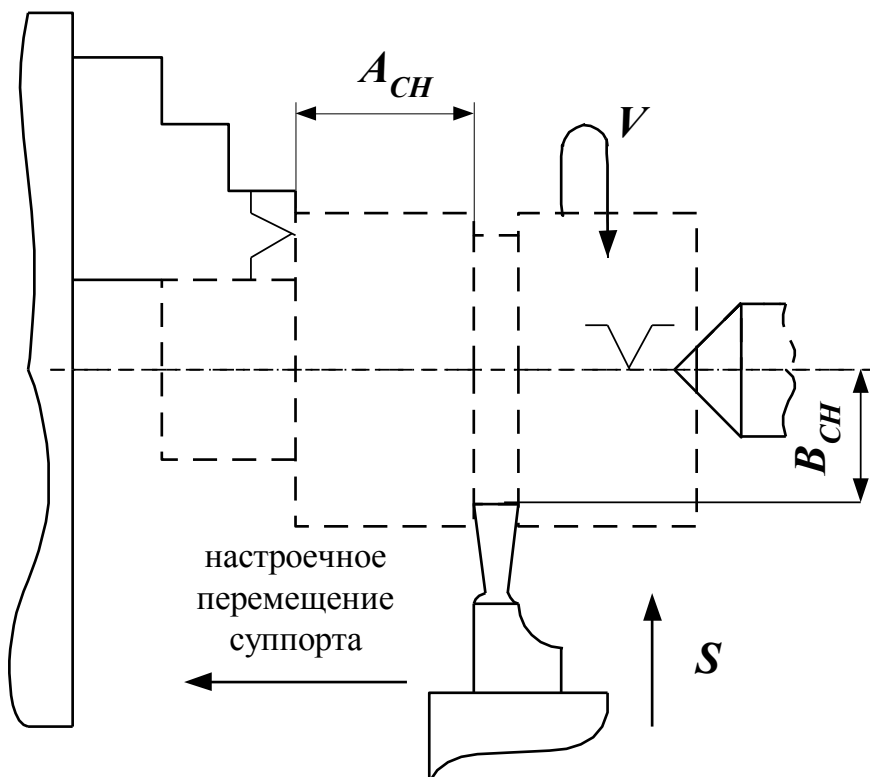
Схема статической настройки технологической системы токарного станка для проточки канавки на расстоянии A_{CH} от исполнительной поверхности кулачка патрона, с которой будет контактировать технологическая база заготовки.
